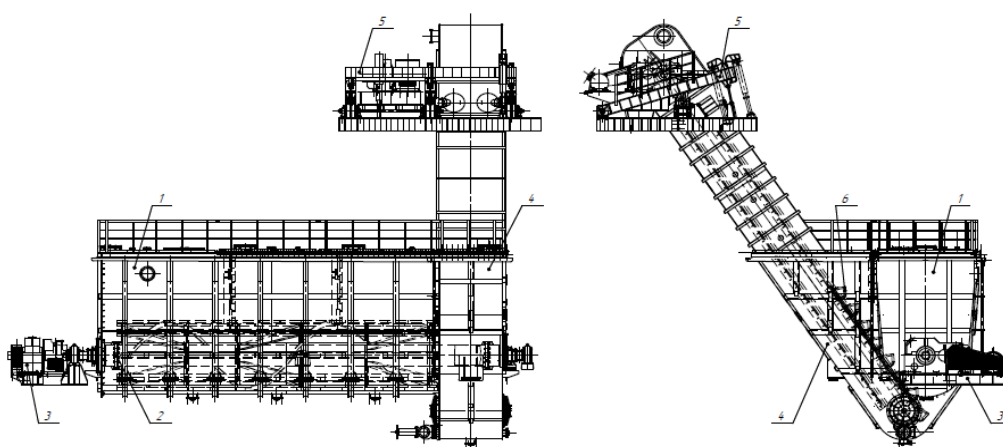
Шнековый растворитель с элеватором: 1 – корпус шнековой мешалки с крышкой, 2 – ротор, 3 – привод шнековой мешалки, 4 – элеватор обезвоживающий, 5 – станция приводная левого исполнения, 6 – цепь ковшовая элеватора
